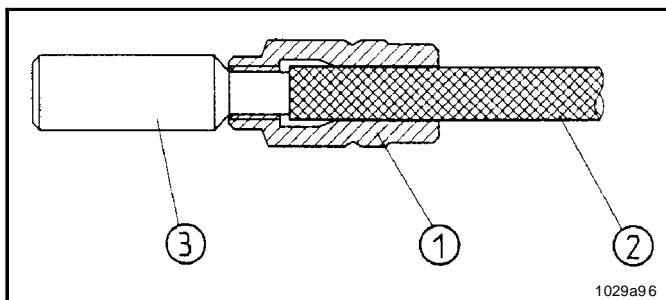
Premontaggio della bussola filettata tramite utensile calibratore
